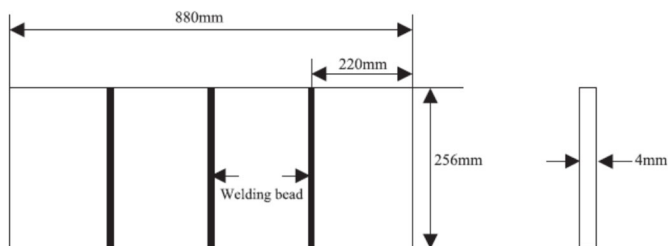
Plattenprobe mit Schweissnähten (aus [56])
